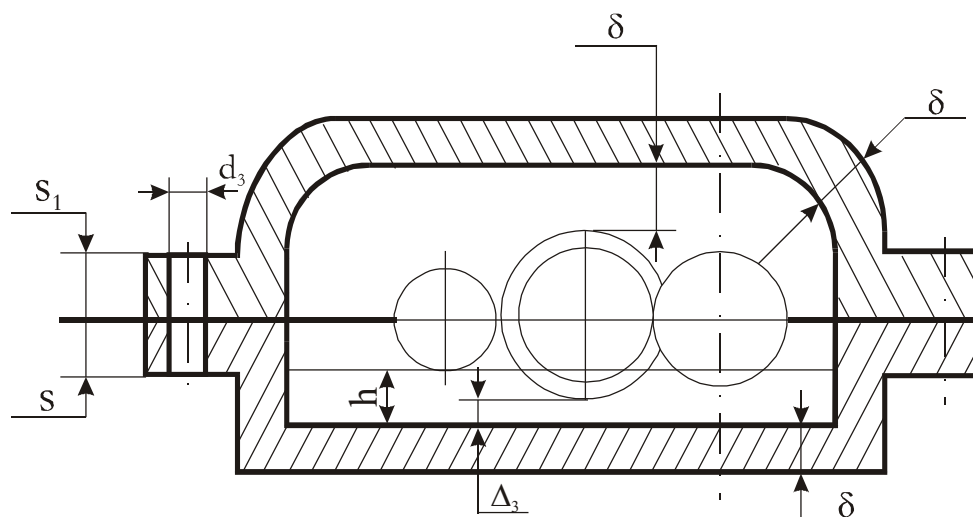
Компонировка крышки и корпуса редуктора
